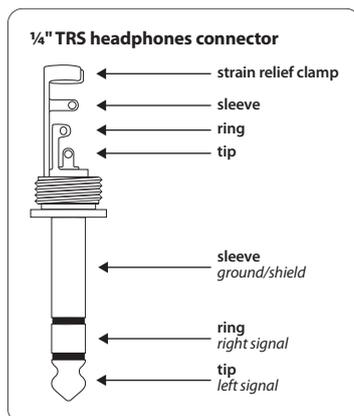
Cablaggio della spina a jack dello stereo per le cuffie ed il CD INPUT
